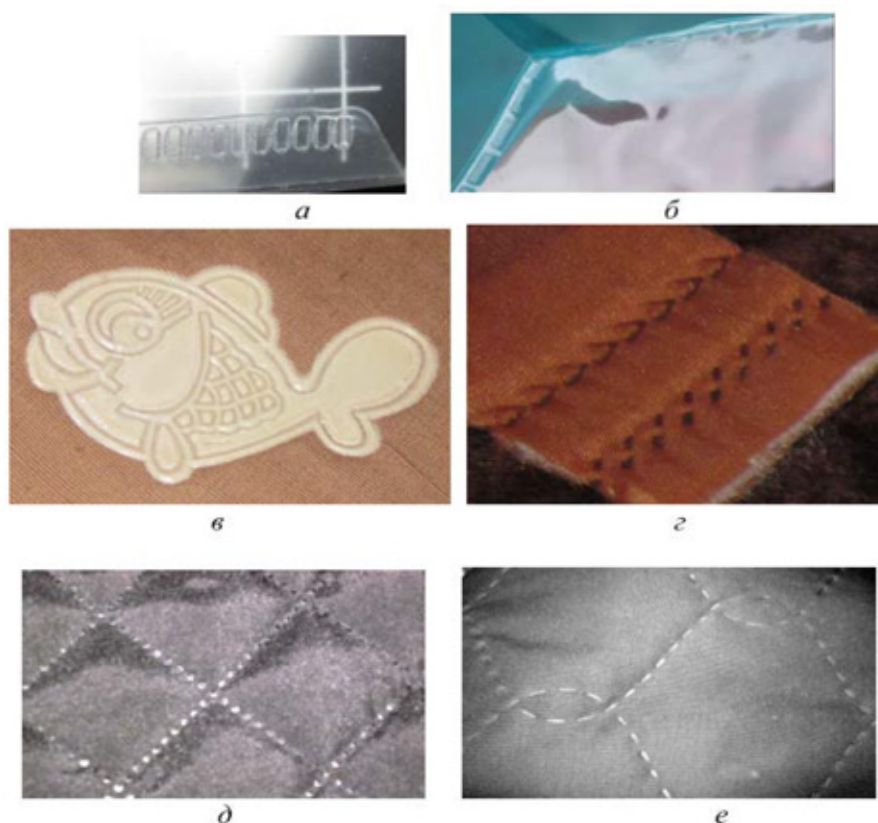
Примеры сварных соединений: а, б — пластиковые упаковки; в — аппликация; г, д, е — выстигивание ткани с утеплителем
